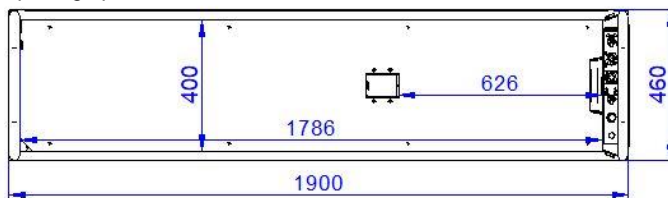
; Dimensions de la plateforme en mm, 2 pantographes
